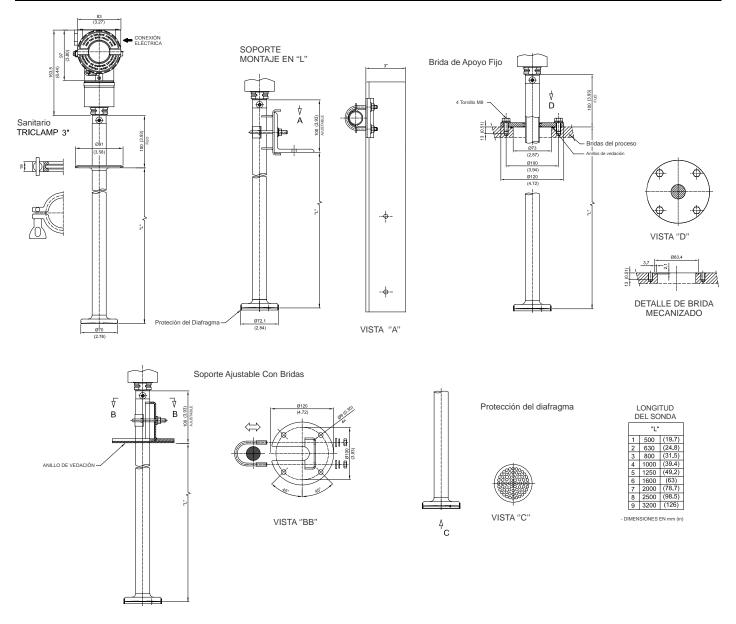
(e) – Diseño Dimensional de Montaje del LD291 – Insersión
